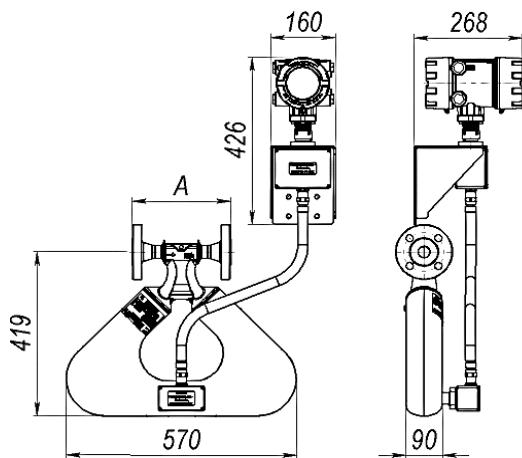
Габаритные и присоединительные размеры преобразователя КТМ СКАЛЯРИС 025
